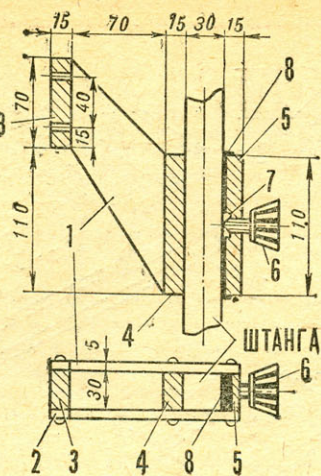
Кронштейн: 1, 2 — боковые стенки, 3, 4, 5 — бруски, 6 — упорный винт, 7 — гайка, 8 — пружинный вкладыш.
